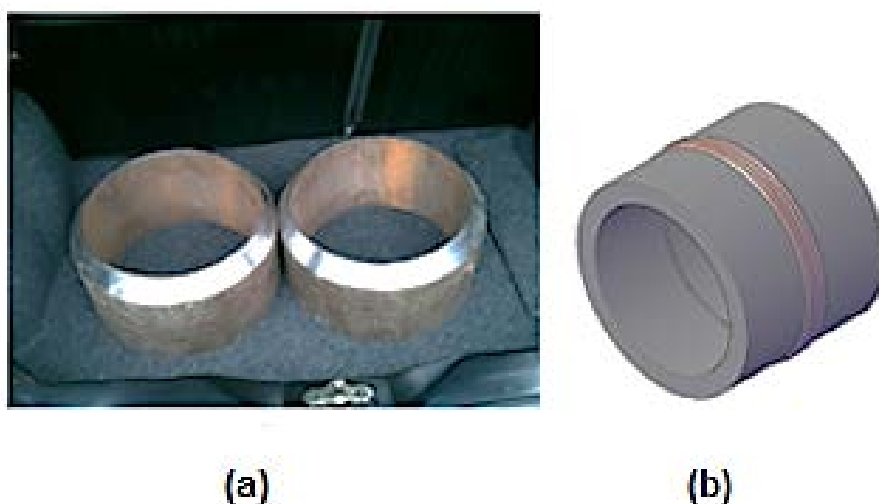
Peça do aço ASTM A 335 Gr P91 preparada para soldagem.
